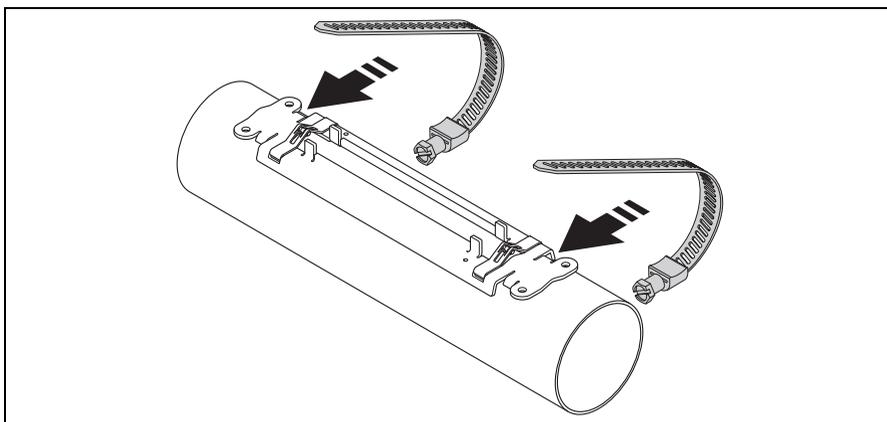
Posizionamento del supporto del sensore e montaggio delle fascette di fissaggio
